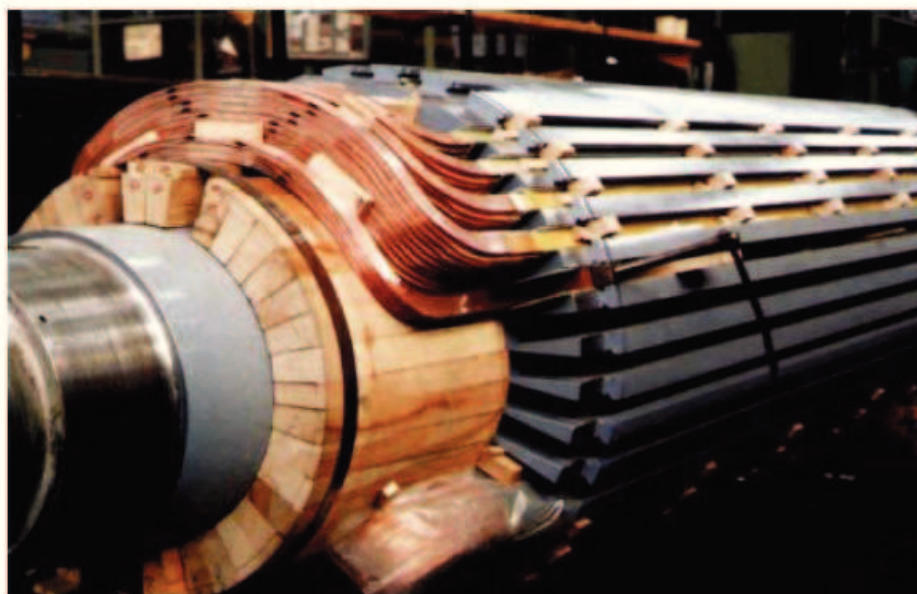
Rotor s vyniklými póly a budičem na hřídeli
